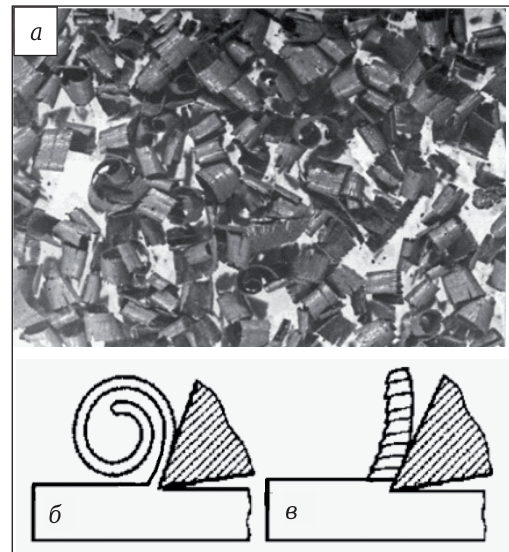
Шихта из стружки термопластичного шликера: а — общий вид; б — схема получения стружки в виде спиралей; в — увеличенный вид схемы стружки
